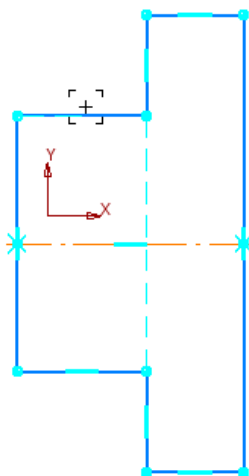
Попереднє креслення деталі для параметричного креслення
